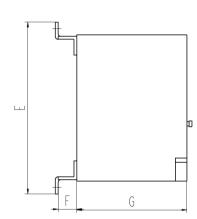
Габаритны и установочные размеры привода моторного МП-300
